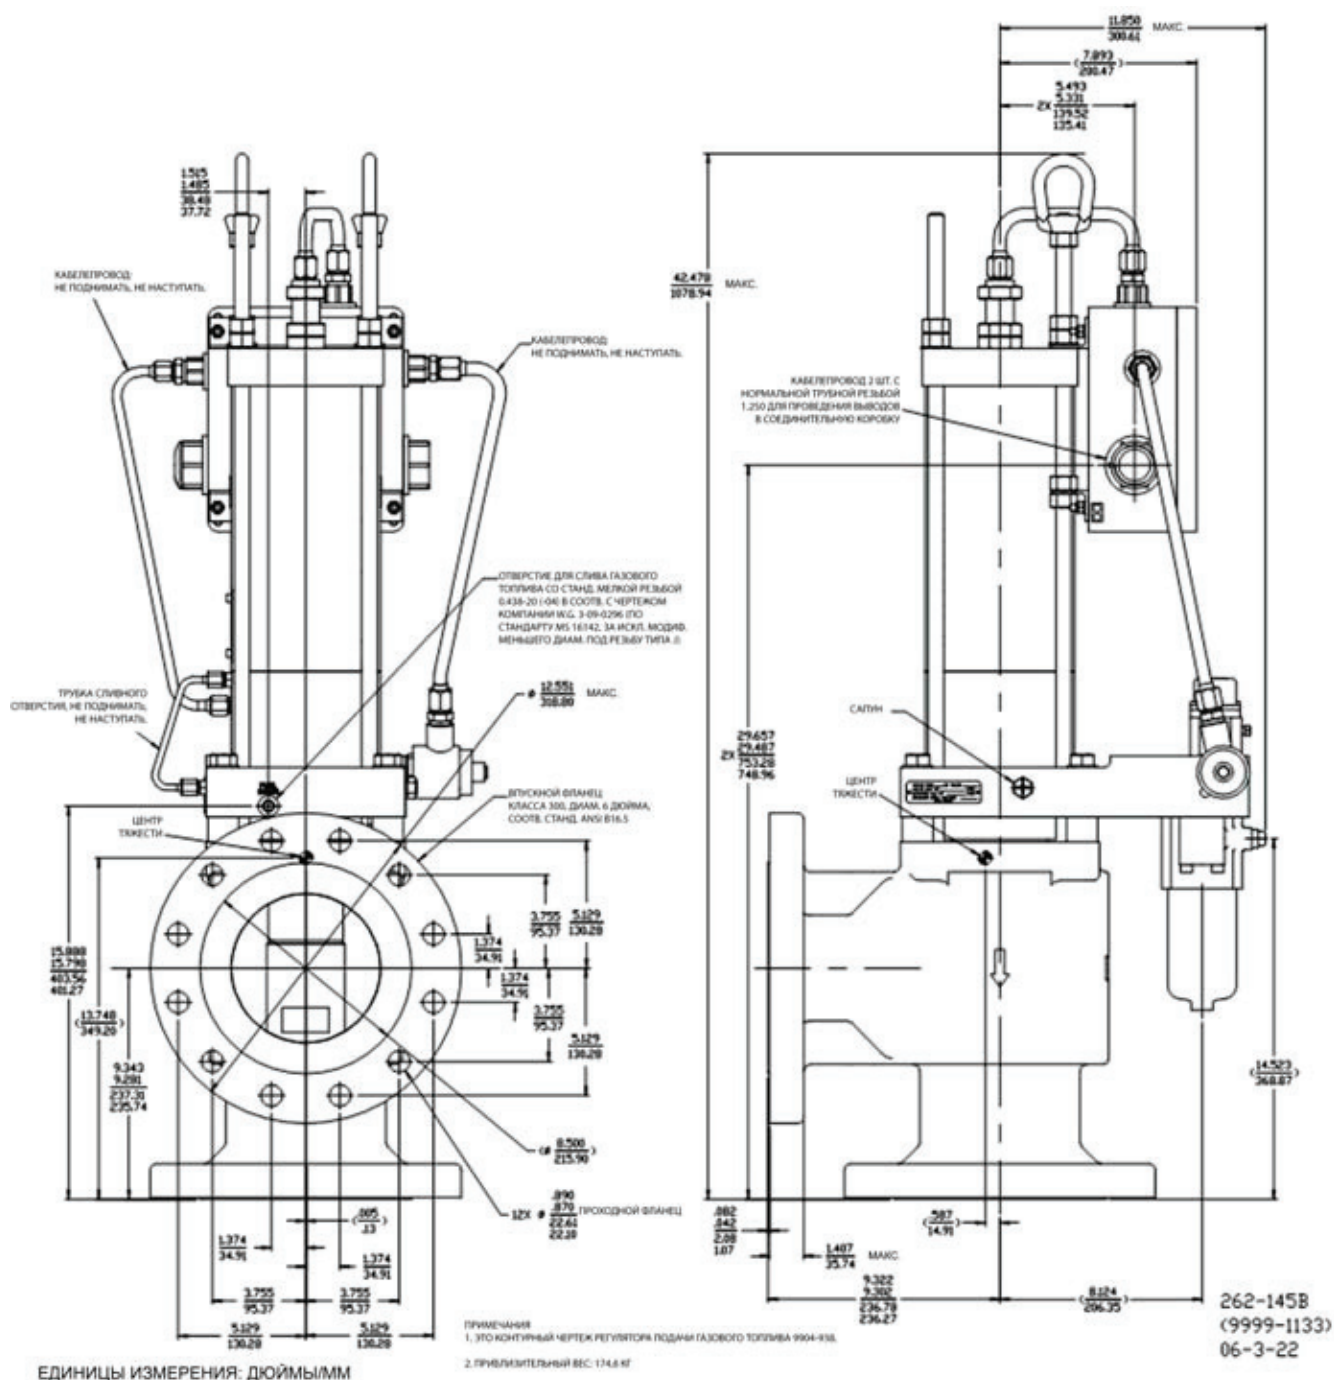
Контурный чертеж регулятора (6 дюймов, двухотверстная соединительная коробка)
